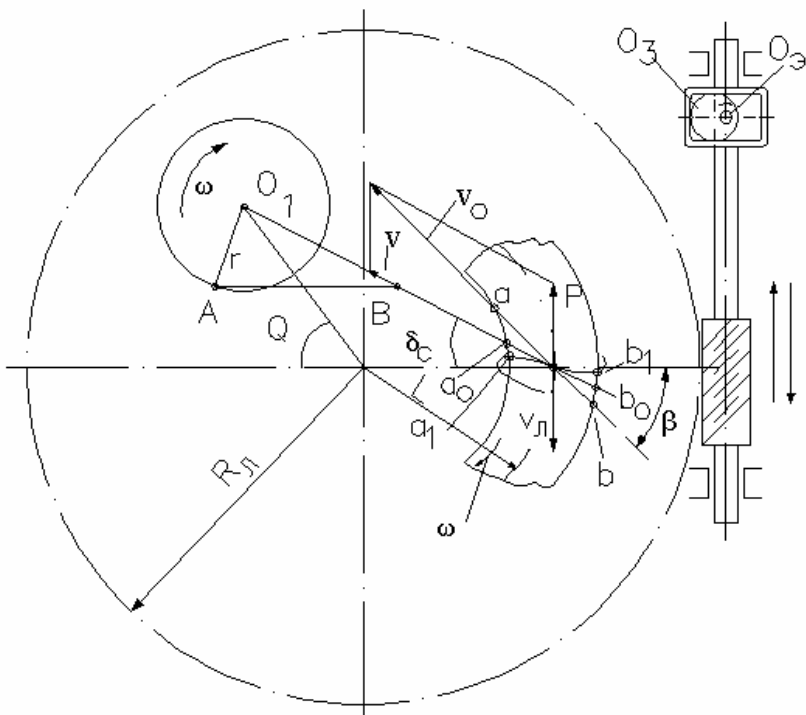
Схема обработки конического зубчатого колеса на станке 5284
